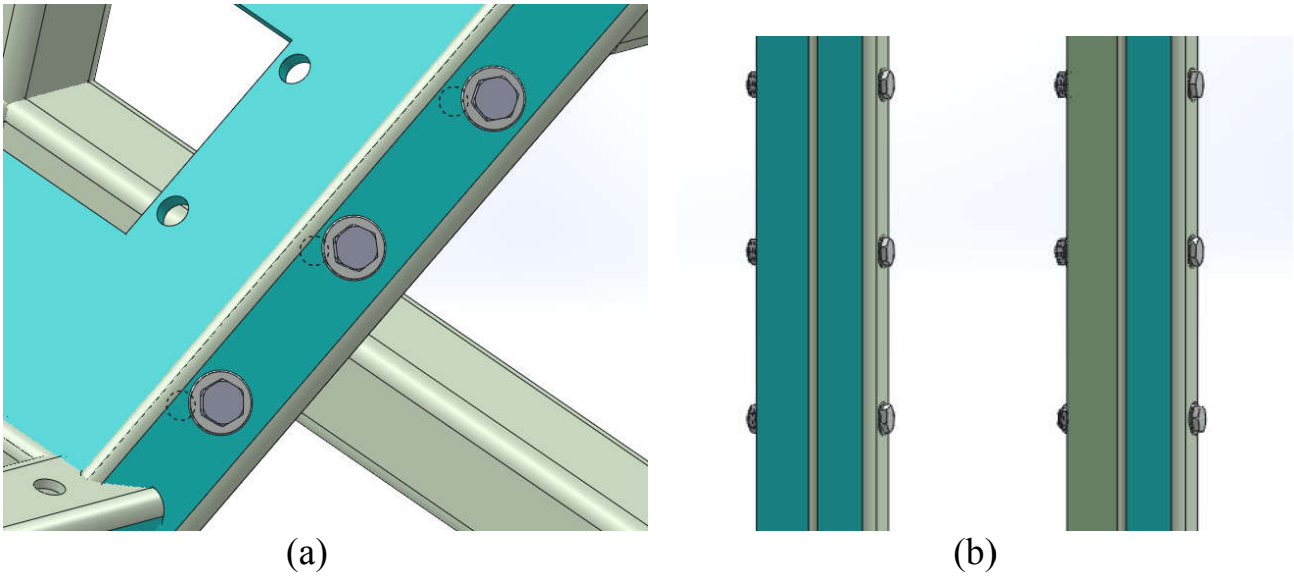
De gauche à droite: (a) assemblage de la plaque avec le bâti, (b) assemblage de porteur de bobine avec le bâti.
